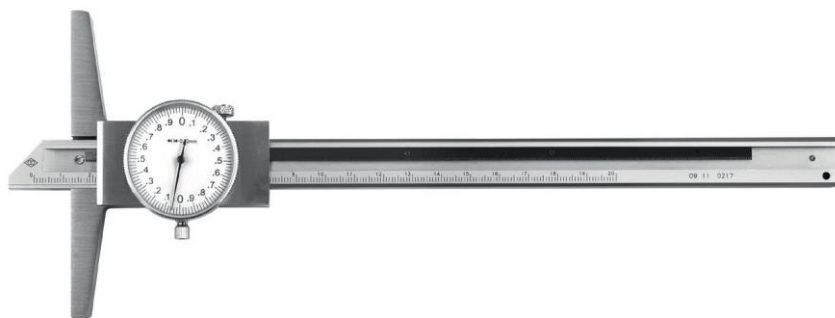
Штангенглубиномер с круговой шкалой ШГК
